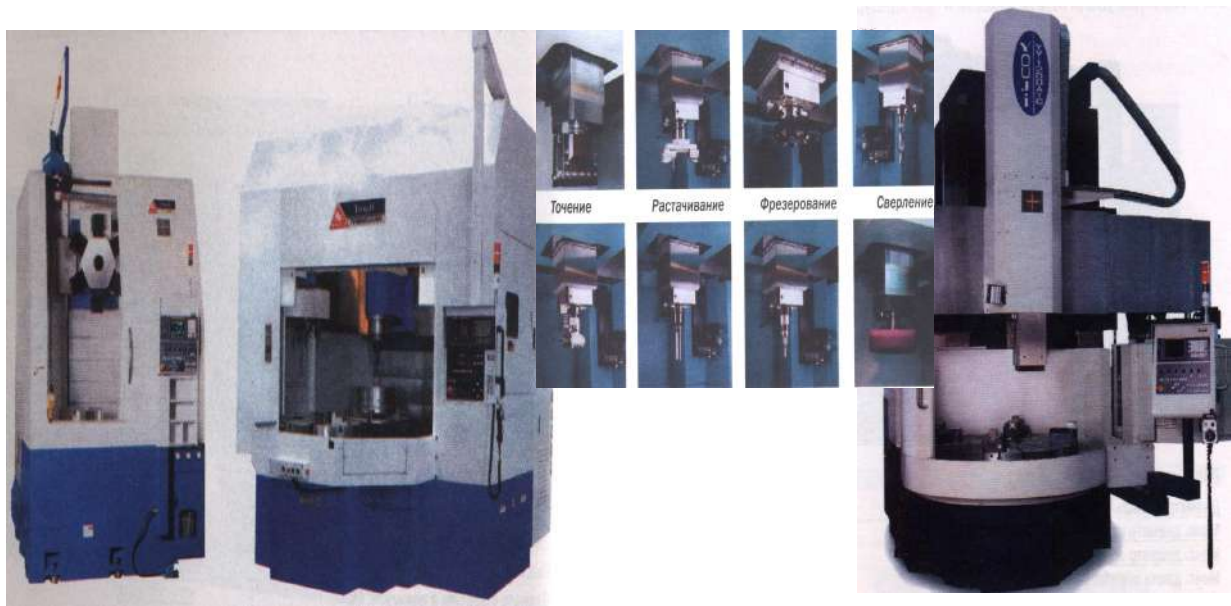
Фрезерні вертикальні верстати серії YV1000-YV1600
